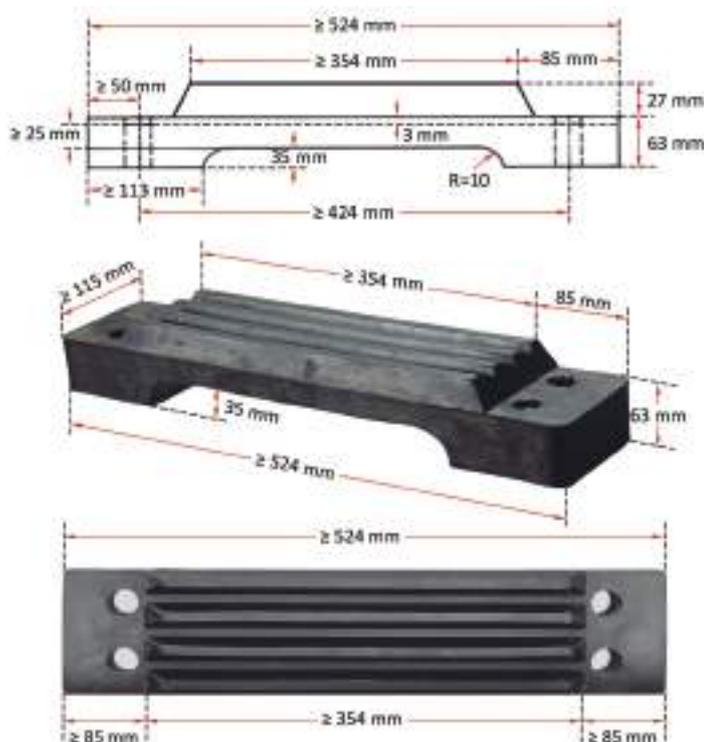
Peldaños de resina sintética: Tipos y dimensiones. (Fuente: impatools.com)
